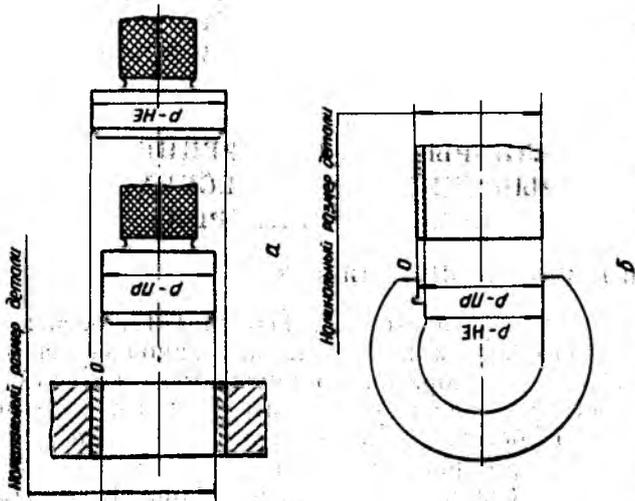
Схема для выбора номинальных размеров предельных гладких калибров: а — калибр-пробка; б — калибр-скоба
